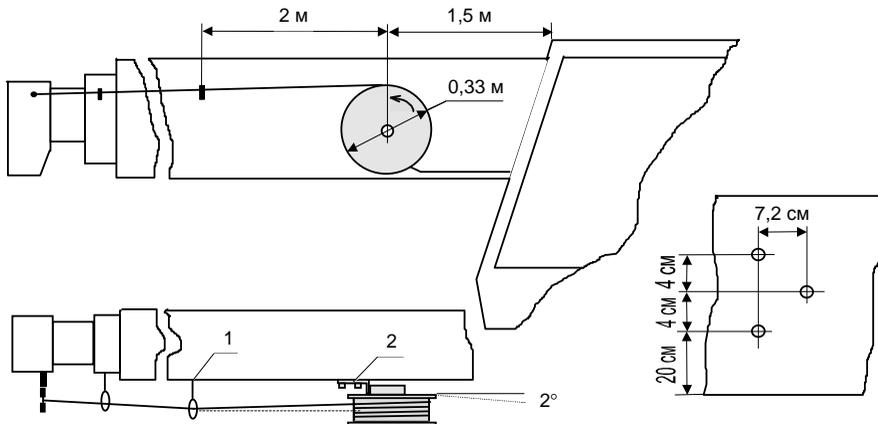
Установка датчика длины стрелы и разметка мест крепления
